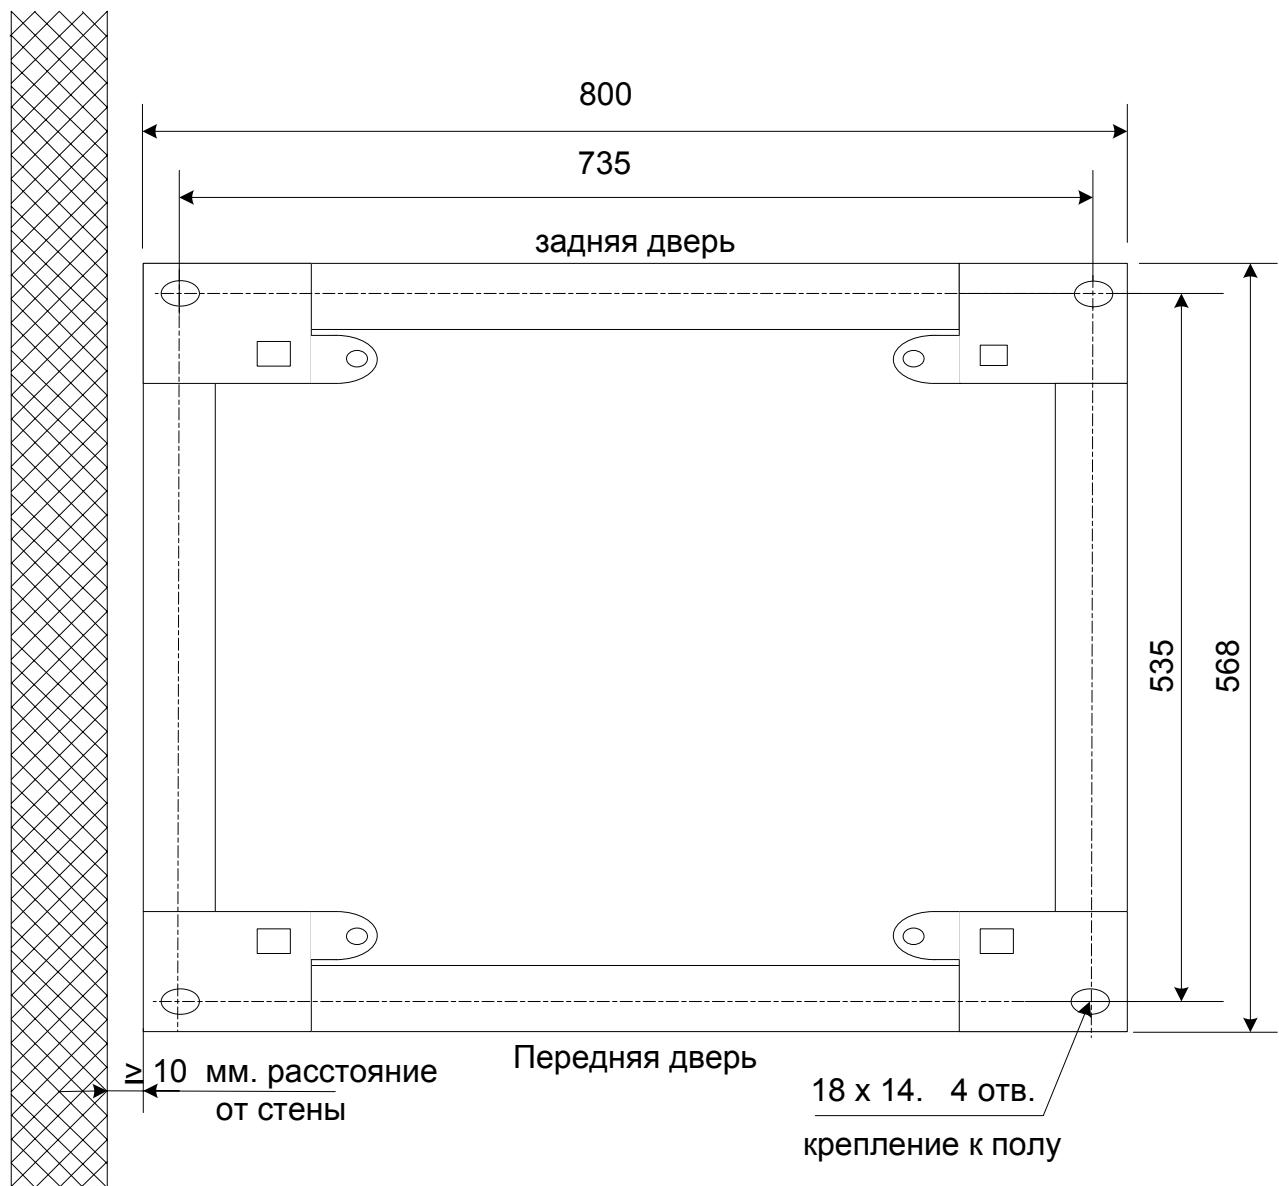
Установочный чертеж напольной стойки БРКУ
